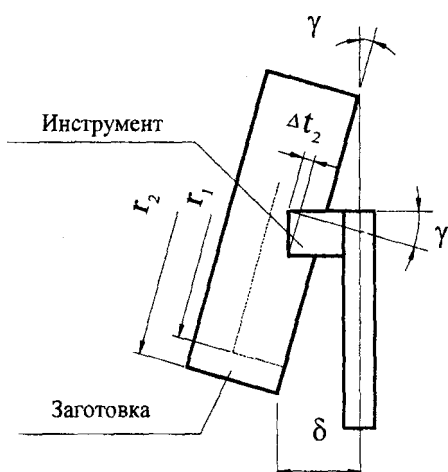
Схема образования погрешности пазов при торцовом биении заготовки
